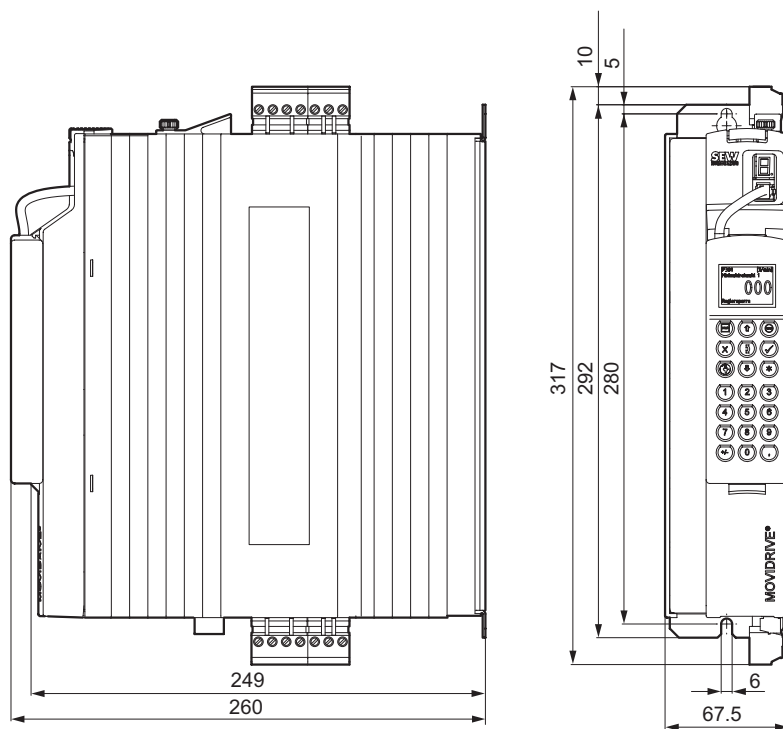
Габаритный чертеж MDX60B, типоразмер 0M, размеры в мм
